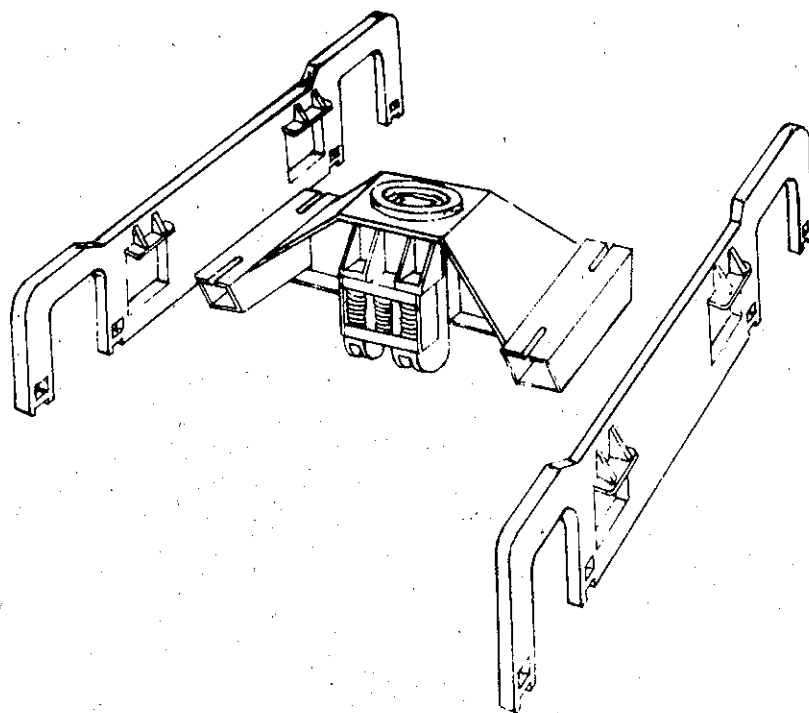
Vue cavalière d'un châssis de bogie de 040 DE 500
